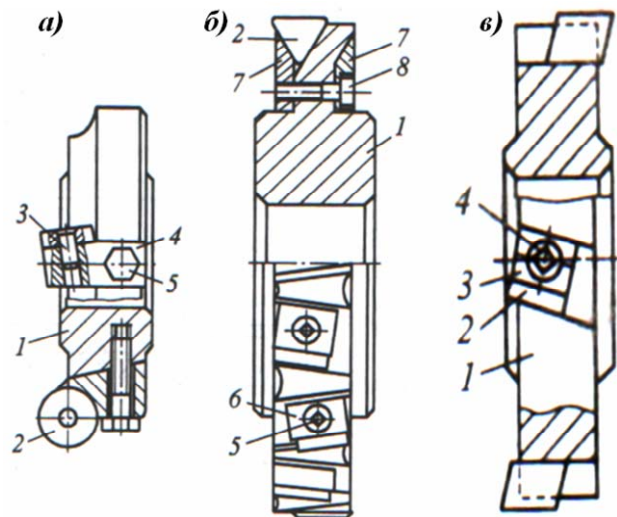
Сборные дисковые фрезы с открытыми базами для крепления СМП
